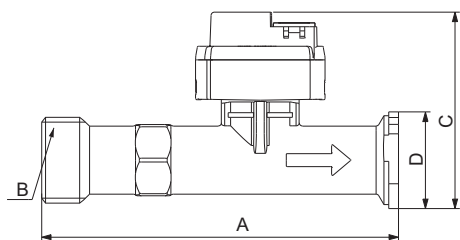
Размеры, VFS QT, 1-12 л/мин, овальный фланец
